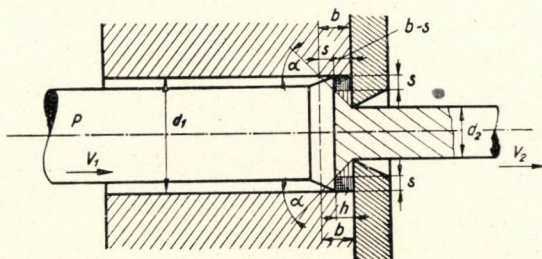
Trichterbildung hinter dem Presswerkzeug
